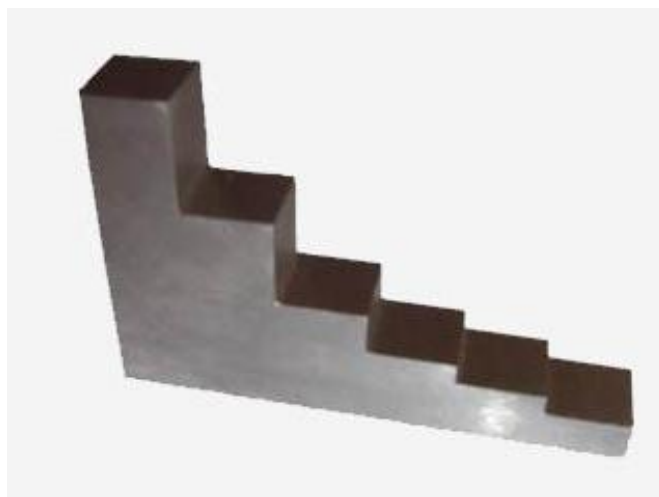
Стандартный образец «ступенька» для ультразвуковой толщинометрии
